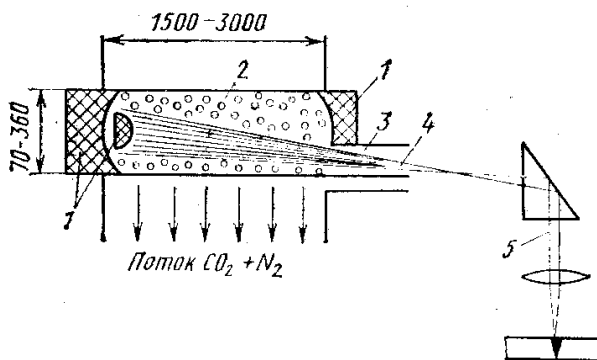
Схема установки для лазерной сварки с газовым лазером:
